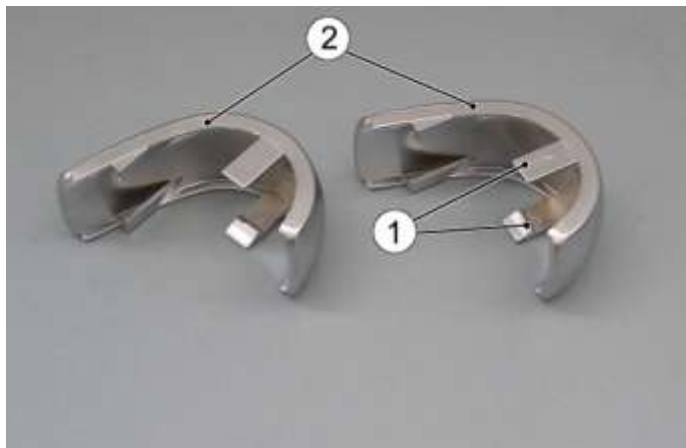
Вставки рукояток КП и раздаточной коробки:
